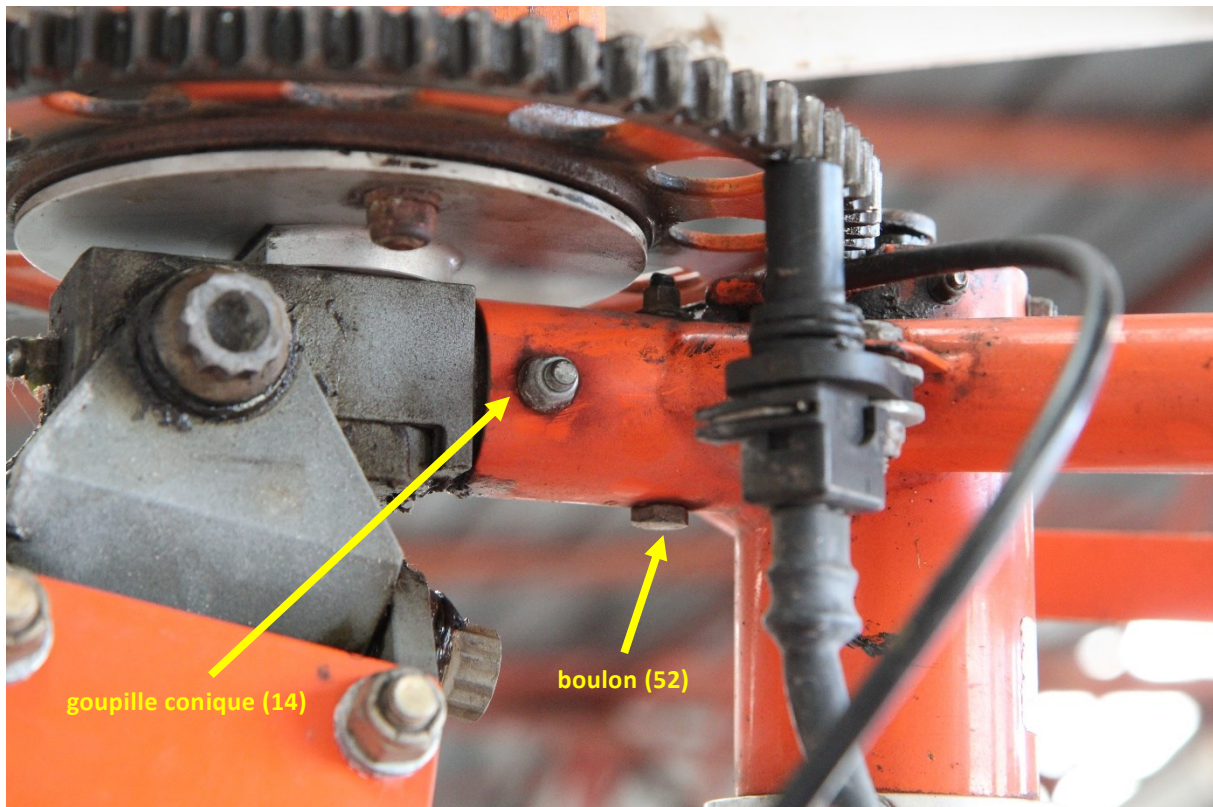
vue rapprochée du boulon (52) et de la goupille (14) sur un Magni M16
